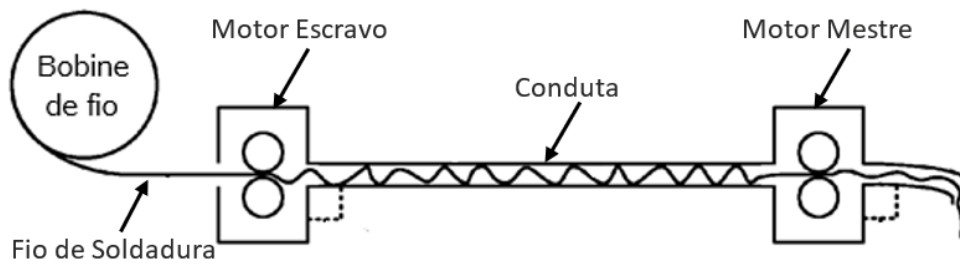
Falhas na alimentação do fio de soldadura [61]
